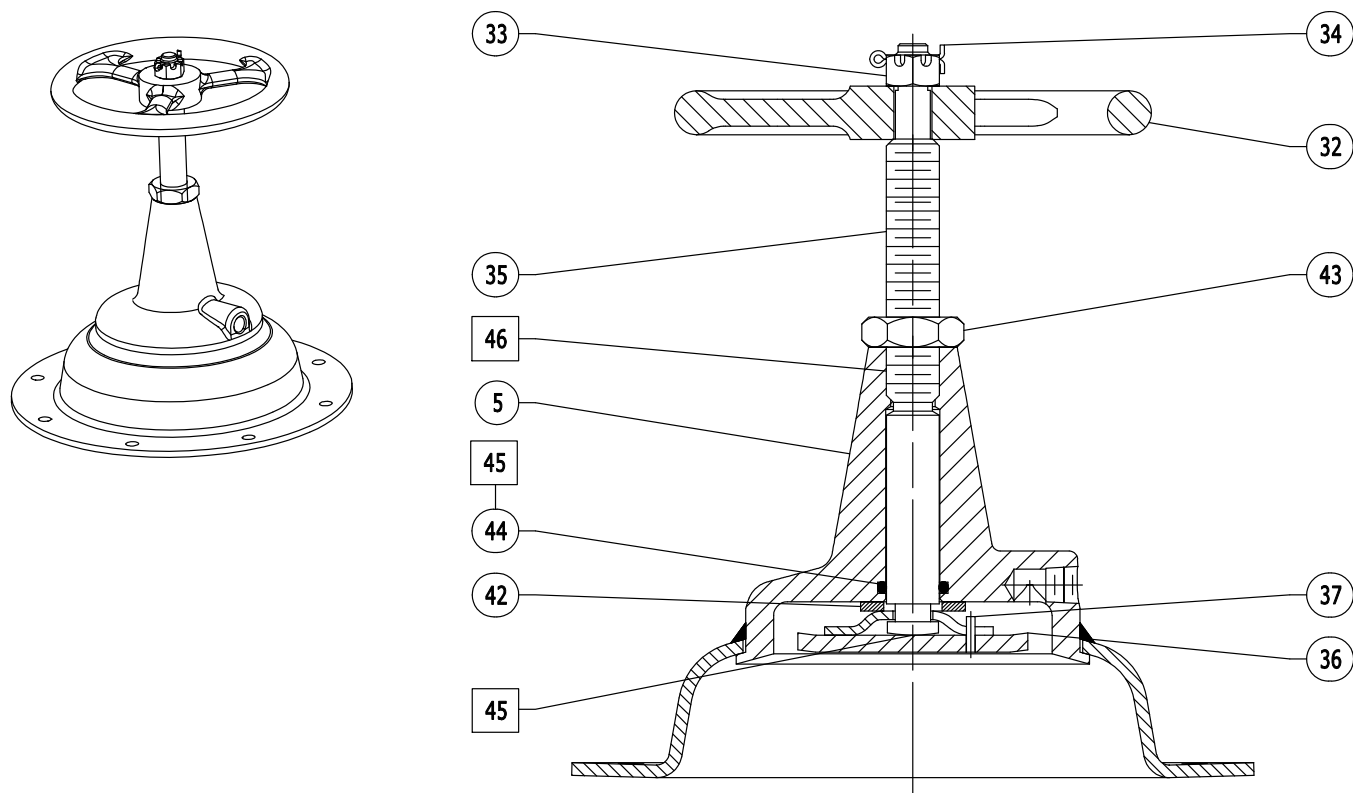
Привод Fisher 2052 размера 3 в сборе
